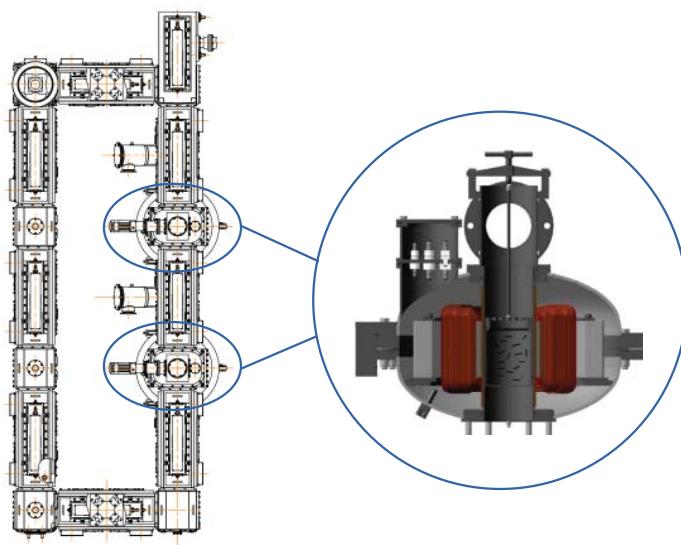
Схема установки вихревого размола порошков [9] и смесителя ABC-150.
